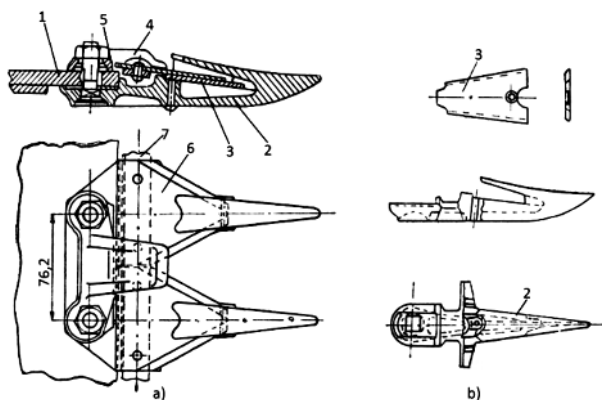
Aparat de tăiere: a – părți componente; b – degetul cu placa contratăietoare
